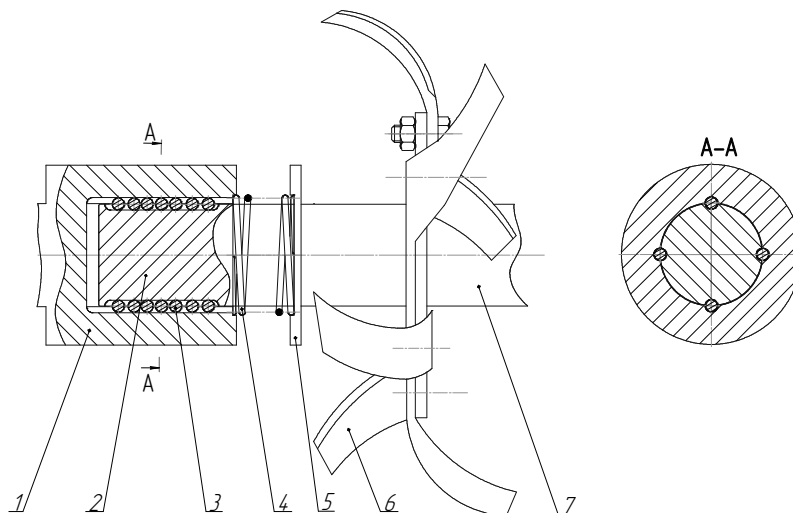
Принципова схема секції вібраційного фрезерного культиватора: 1 – опора; 2 – цапфа вала; 3 – кульки; 4 – пружина; 5 – шайба упорна; 6 – фреза; 7 - вал.
